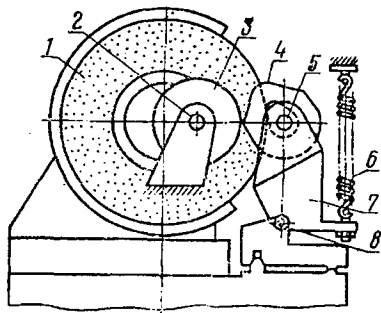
Схема верстата для шліфування кулачків розподільного валу: 1 – шліфувальний круг; 2 – вісь; 3 – ролик; 4 – копір; 5 – шпіндель; 6 – пружина; 7 – люлька; 8 – вісь.
